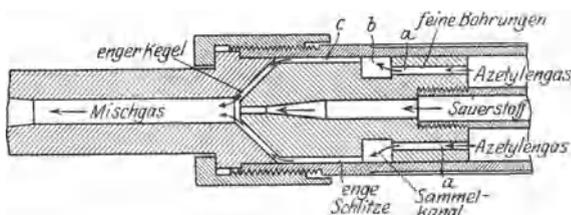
Schweißbrenner mit Rückschlagsicherung.
